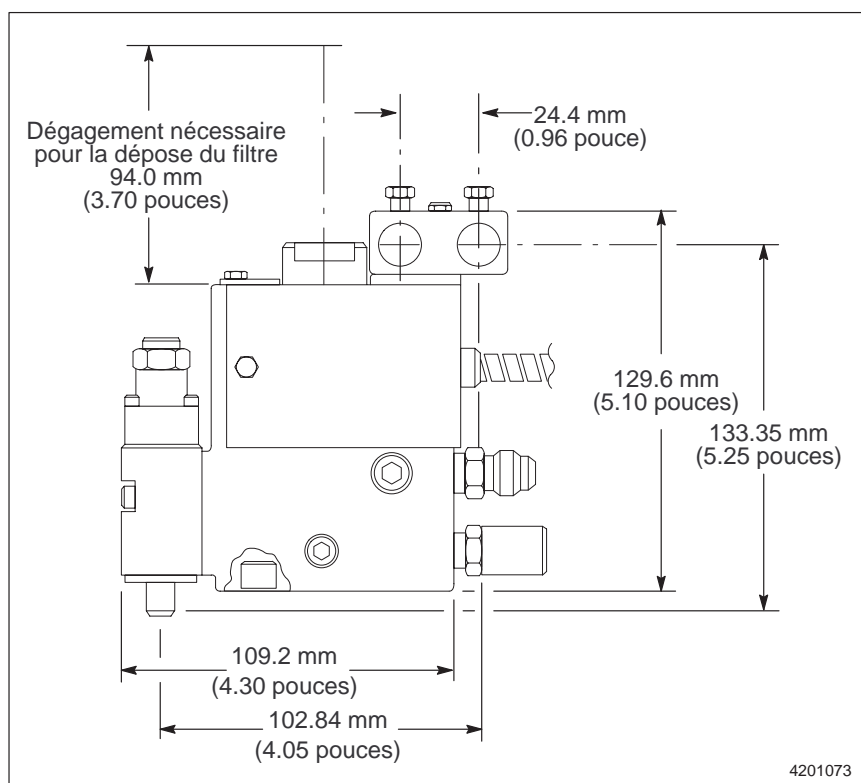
Dimensions d'un pistolet H-200 à filtre intégré
